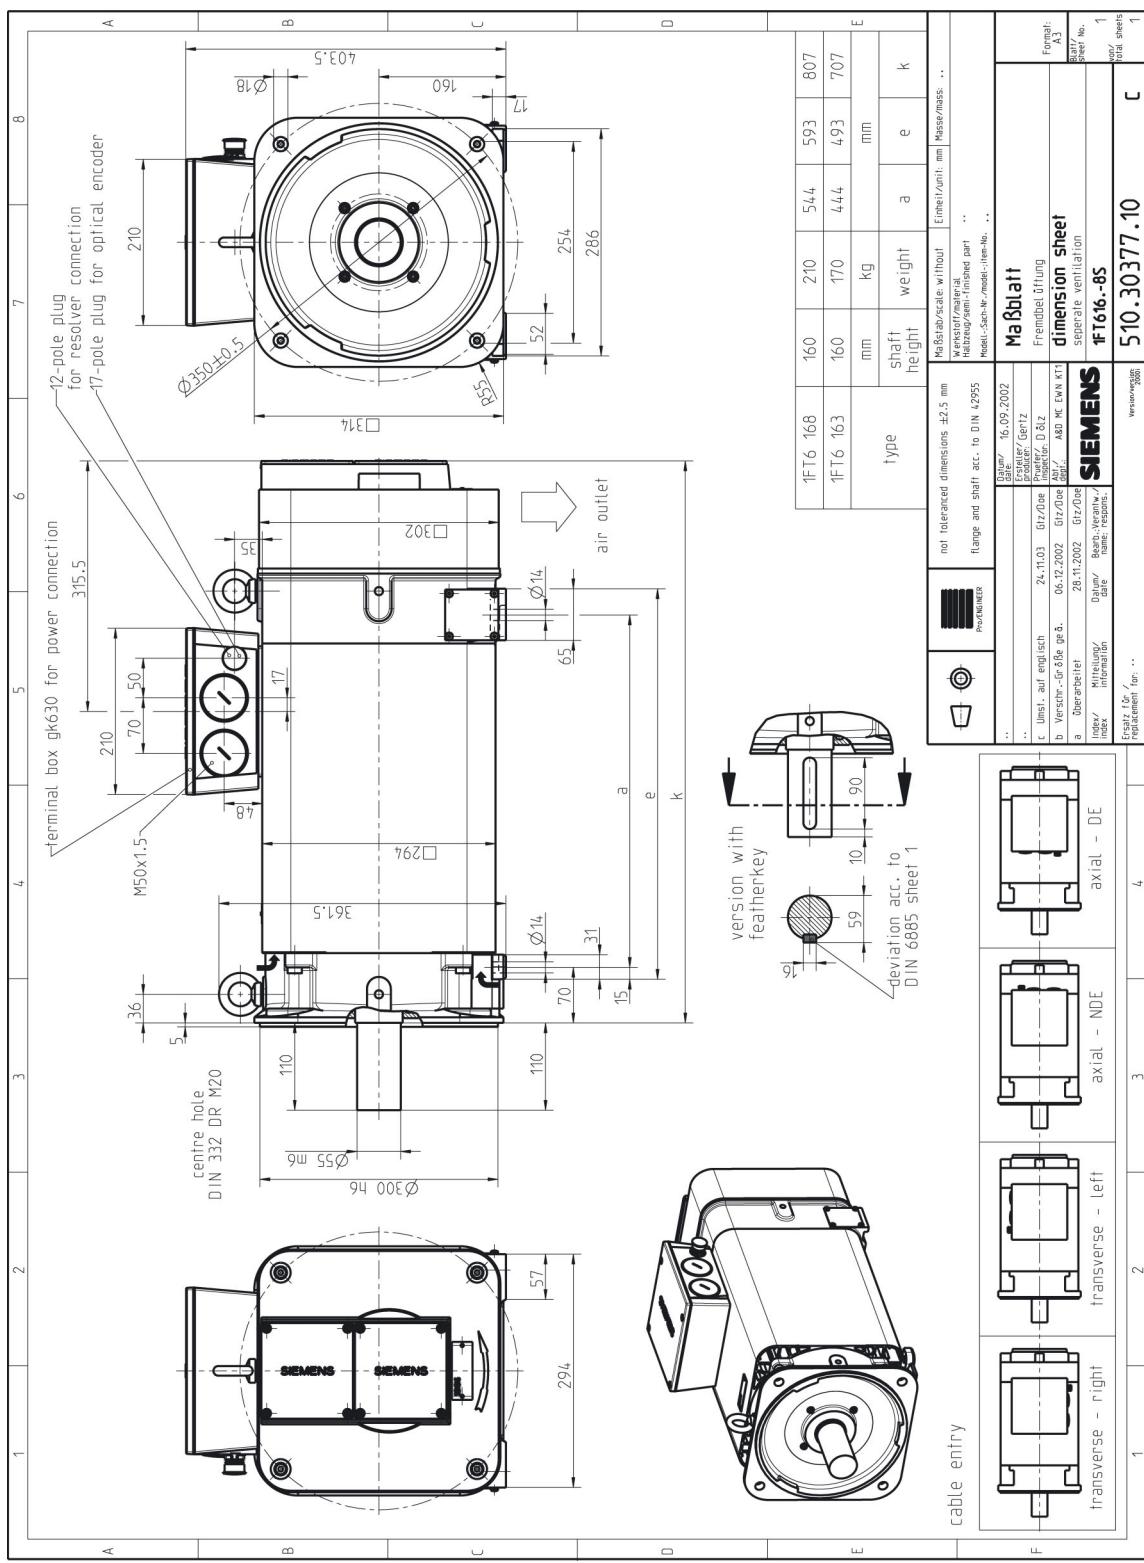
1FT616□ fremdbelüftet mit Klemmenkasten
